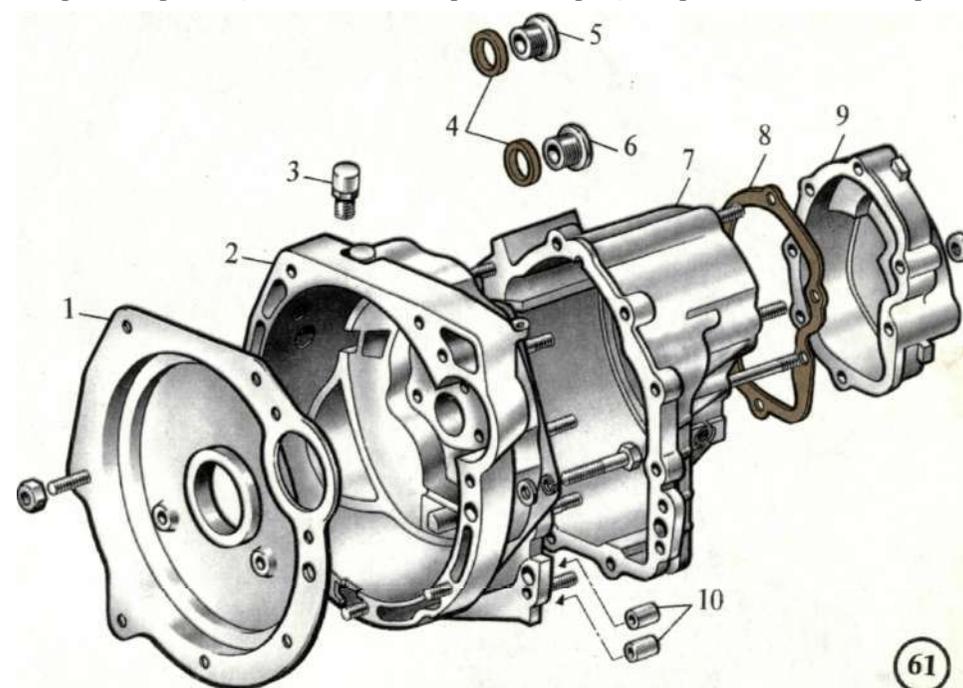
Картеры сцепления, коробки передач и главной передачи:
